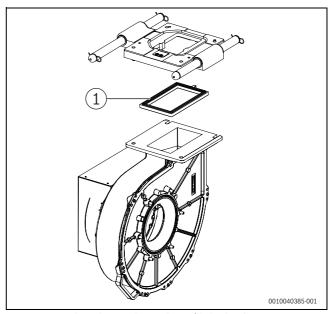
Remplacer le joint du ventilateur/de la glissière
